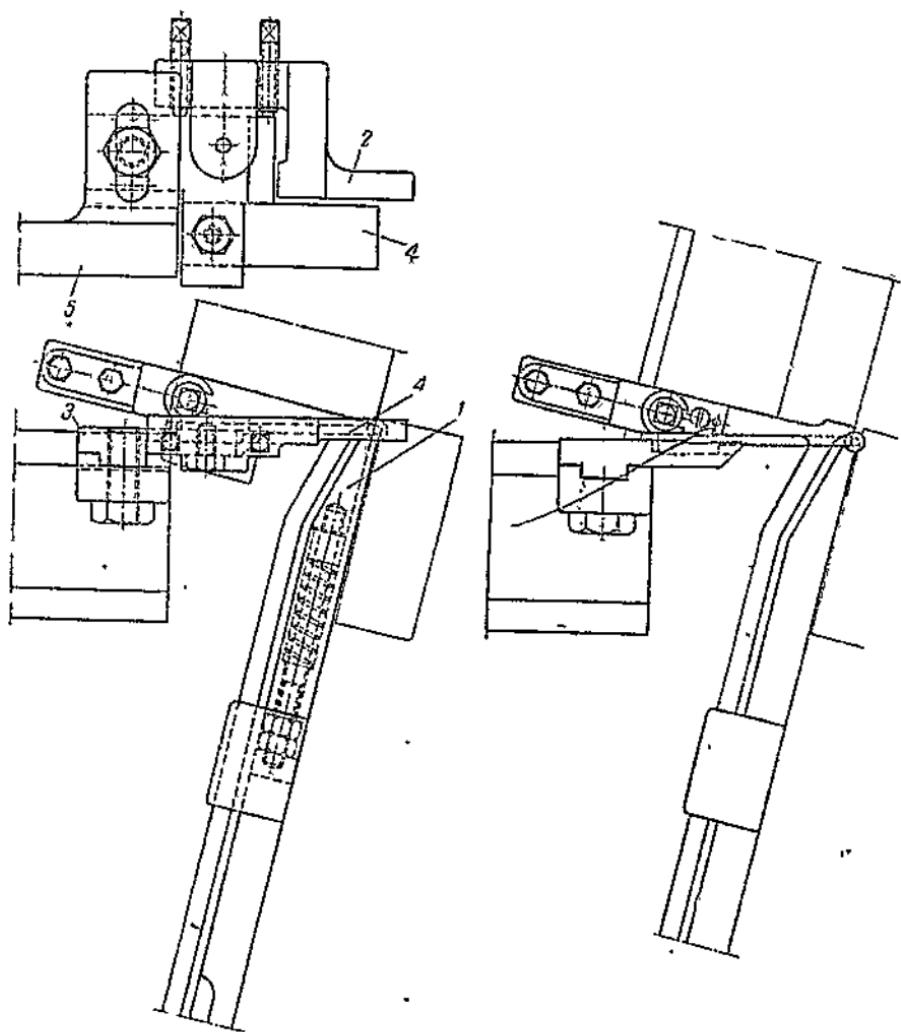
Резьбонакатный автомат Кайзер (вид спереди).
